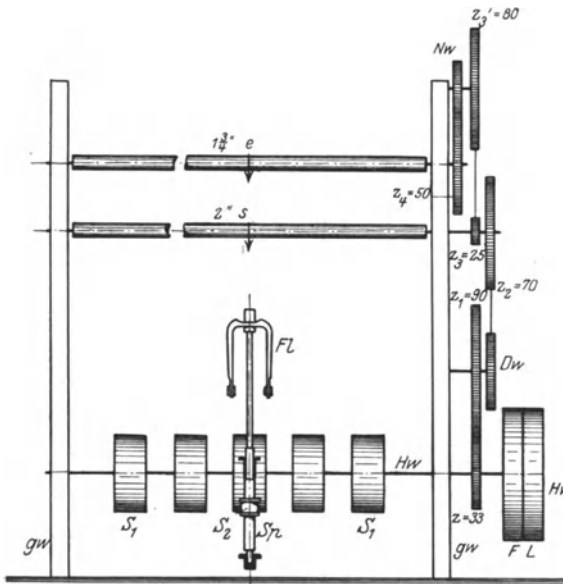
Getriebebeskizze zur Hechelspinnmaschine.
